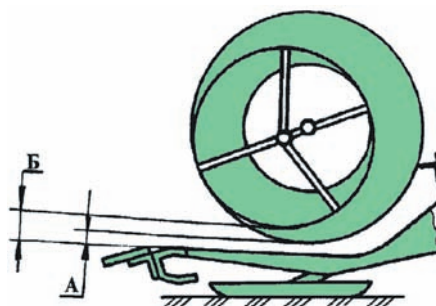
Схема расположения шнека и его пастьково-го механизма при работе жатки. А-зазор между спиралью шнека и днищем корпуса; Б-зазор между пальцами пастьково-го механизма и днищем корпуса
